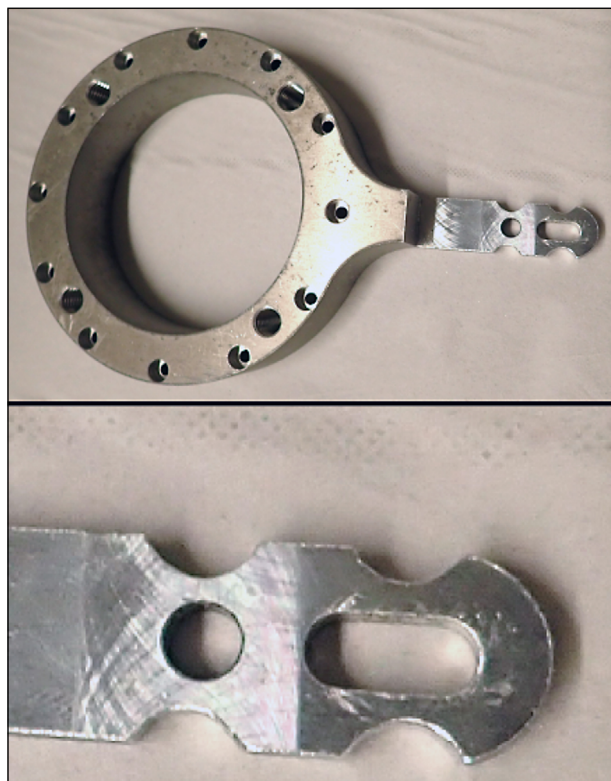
Angepasste Einbaulehre mit Aussparungen für Madschrauben
